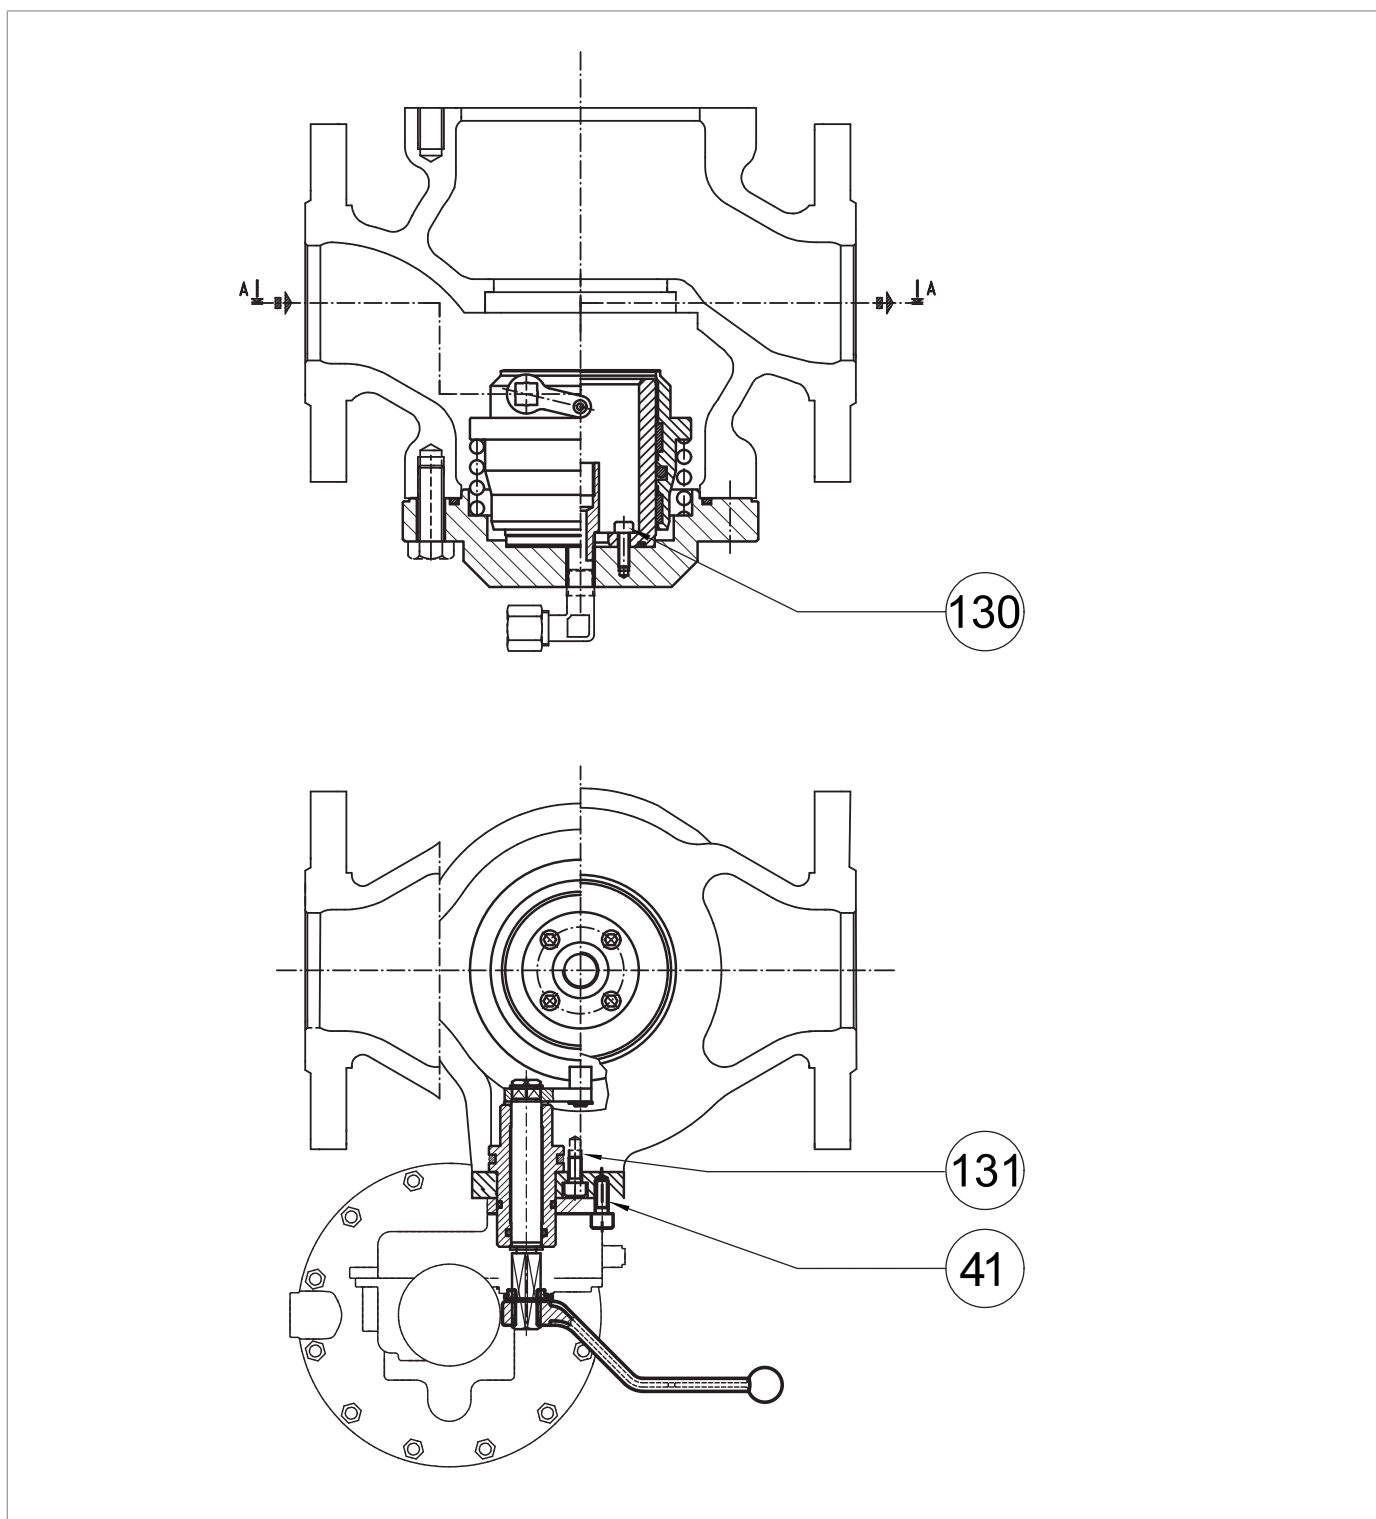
Coppie di serraggio valvola di blocco SA
